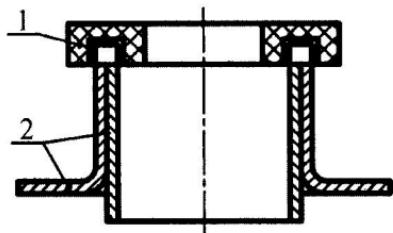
Високочастотне зварювання плавленням без тиску: 1 – індуктор; 2 – заготовки, що зварюються
